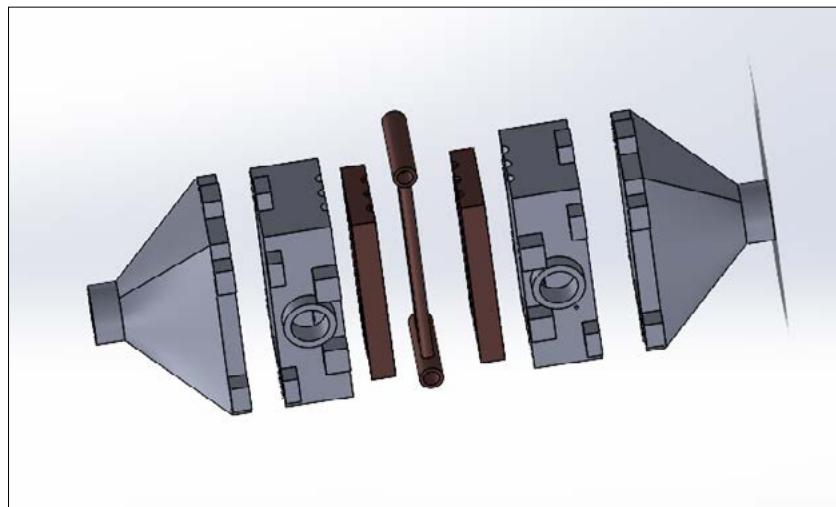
Vista de las secciones del intercambiador de calor elaborado con SolidWorks. [5]
